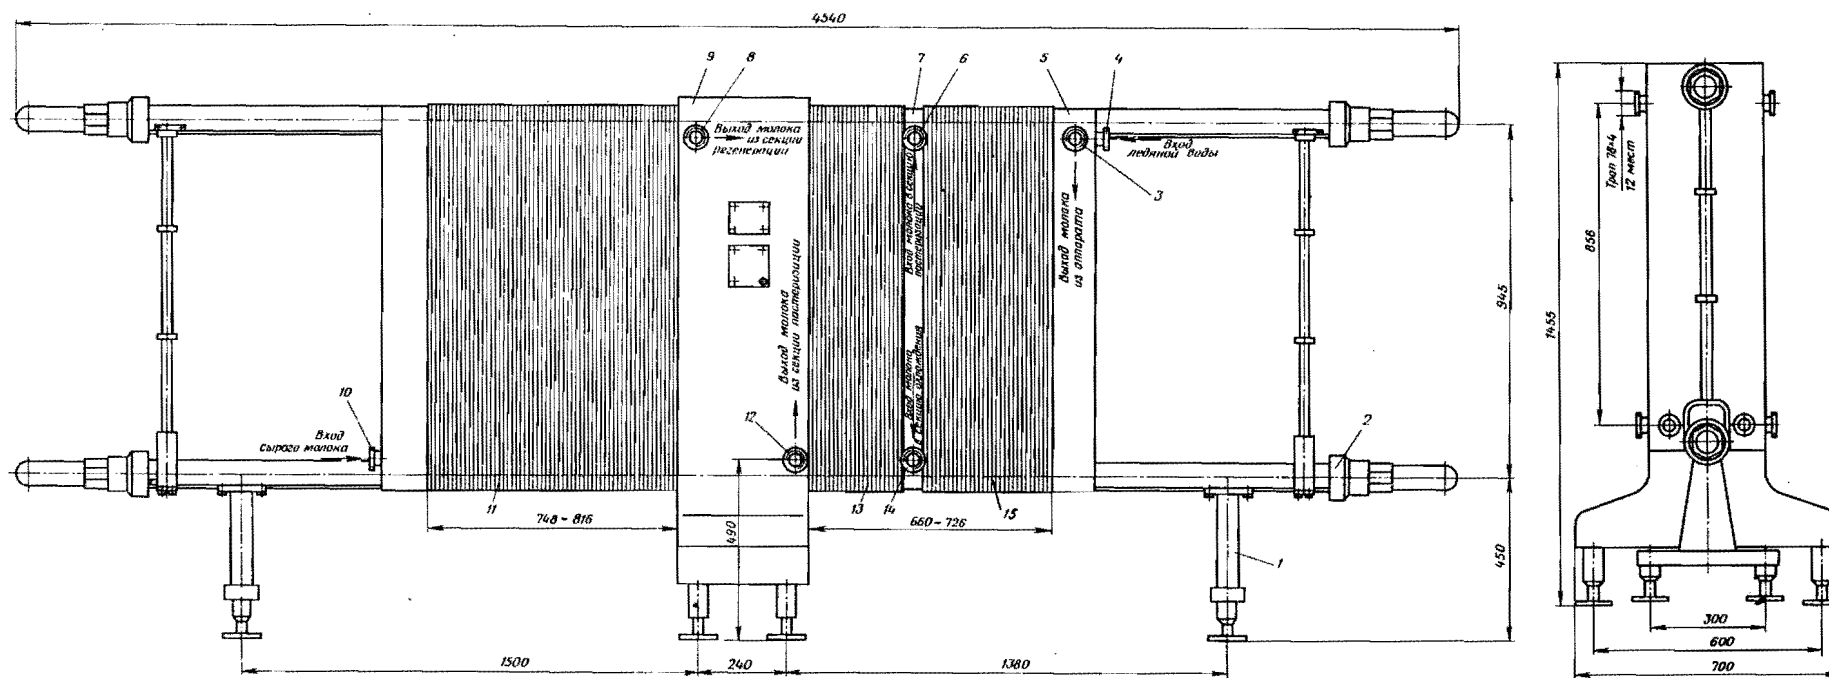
Общий вид пластинчатого аппарата установки марки А1-ОКЛ-10:
